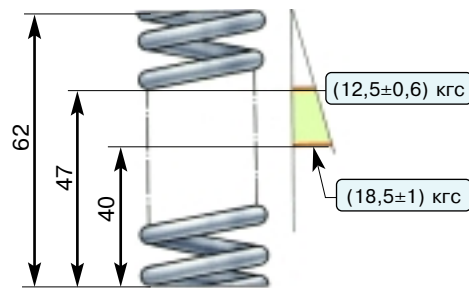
Основные данные для проверки пружины натяжителя двигателя мод. 2106–70
